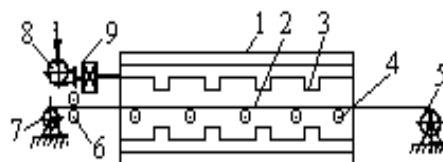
Схема сушилки для ткани или пленочного материала с сопловым обдувом: 1 - камера; 2 - пленочный материал; 3 - сопла; 4 - ролики; 5 - намоточное устройство; 6 - наносное устройство; 7 - разматочное устройство; 8 - вентилятор; 9 - калорифер
